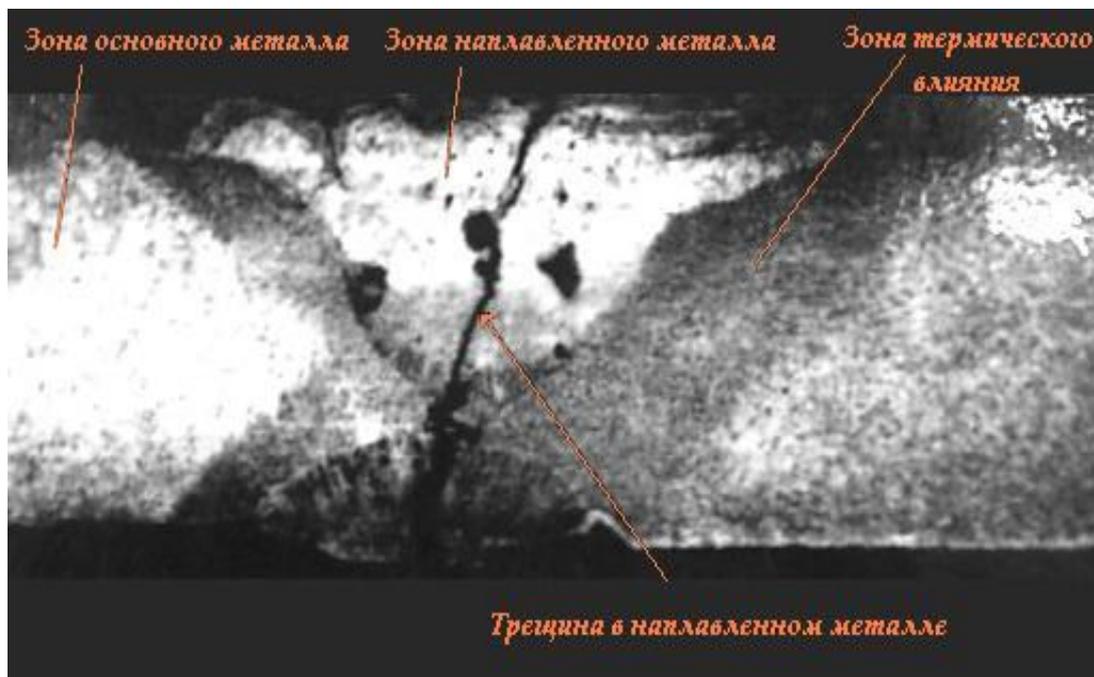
Дефекты и повреждения, при сварке.
